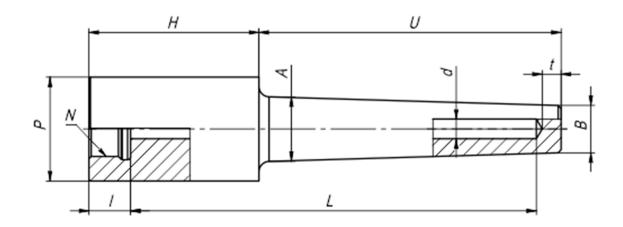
Гильза под приварку через адаптер (Socket Weld), цельноточёная, коническая, под подвижный штуцер.
